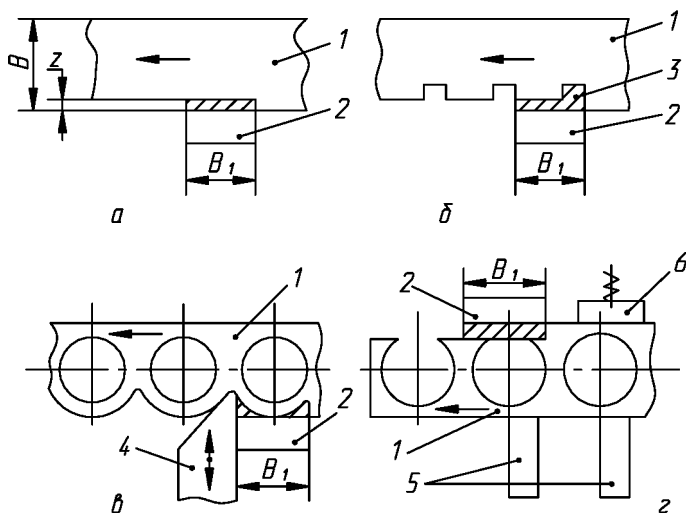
Конструктивные формы шаговых ложей: 1 — полоса, 2 — шаговый нож, 3 — выступ для предотвращения образования «усика», 4 — подвижной упор, 5 — временные упоры, 6 — боковой прижим
